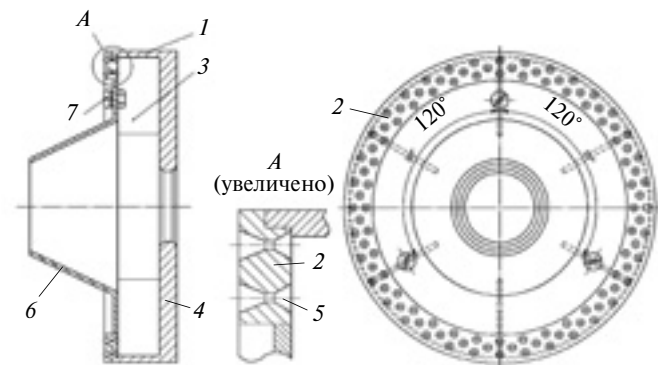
Алмазный шлифовальный круг с коническими отверстиями для торцевого шлифования
